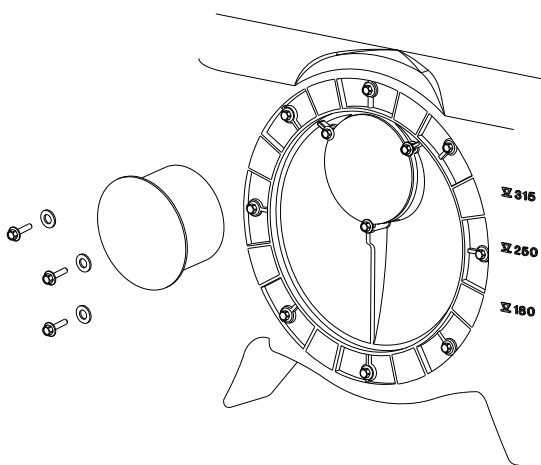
Śruba w pierścieniu zewnętrznym przed dokręceniem
